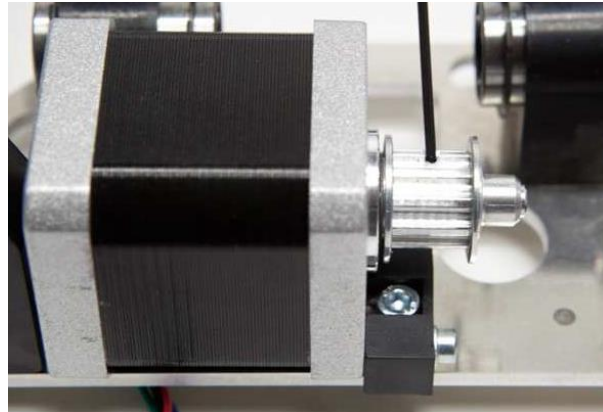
Motor de paso a paso que llevará a cabo el movimiento en el eje
